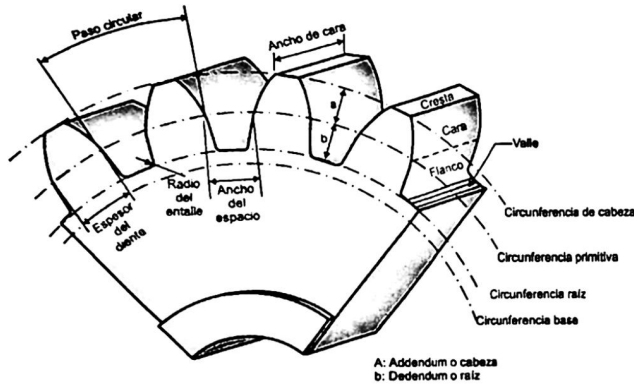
Partes de un engrane cilíndrico de dientes rectos.
